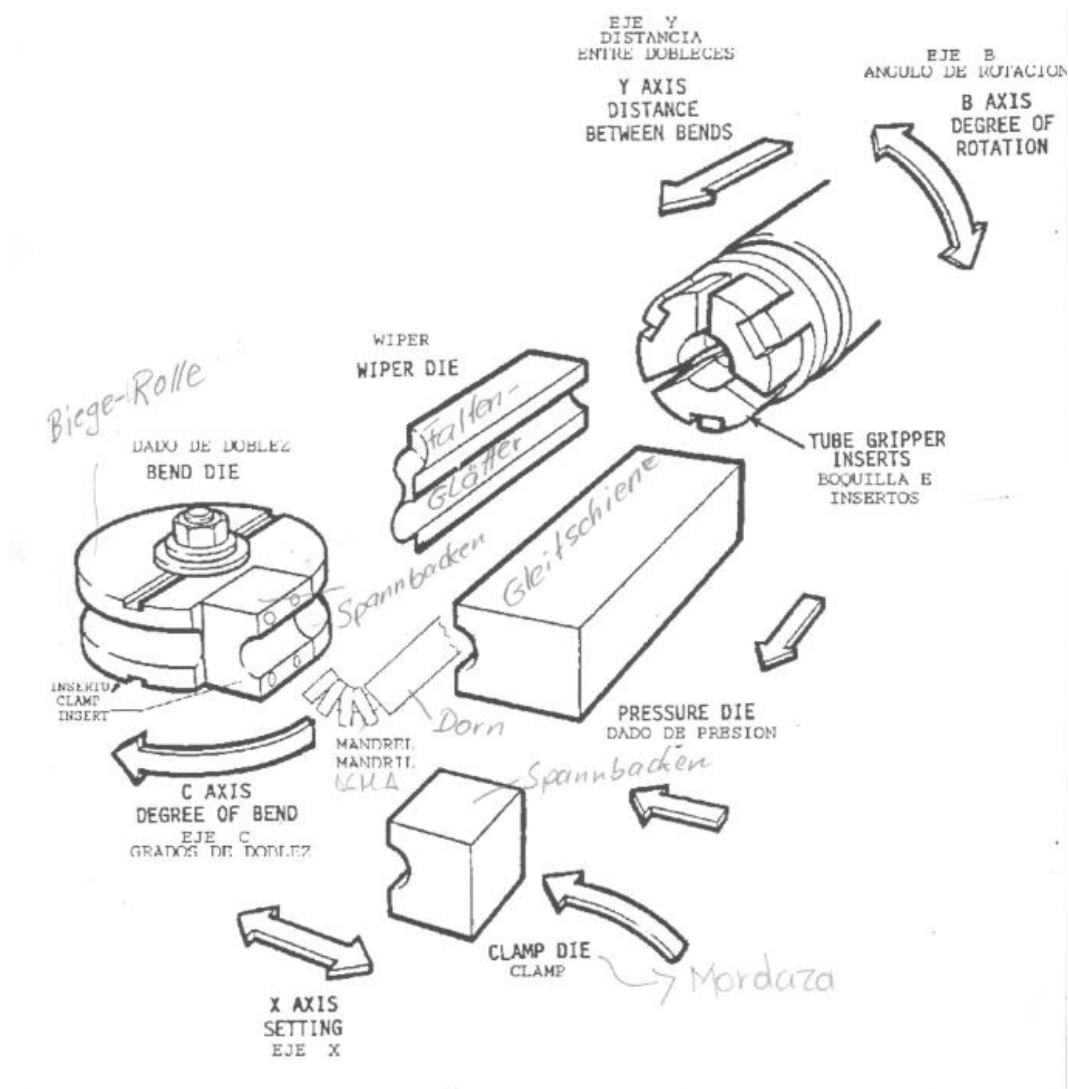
Herramental para dobladora de tubo CNC "Cortesía MEPEPSA/ATSA"
